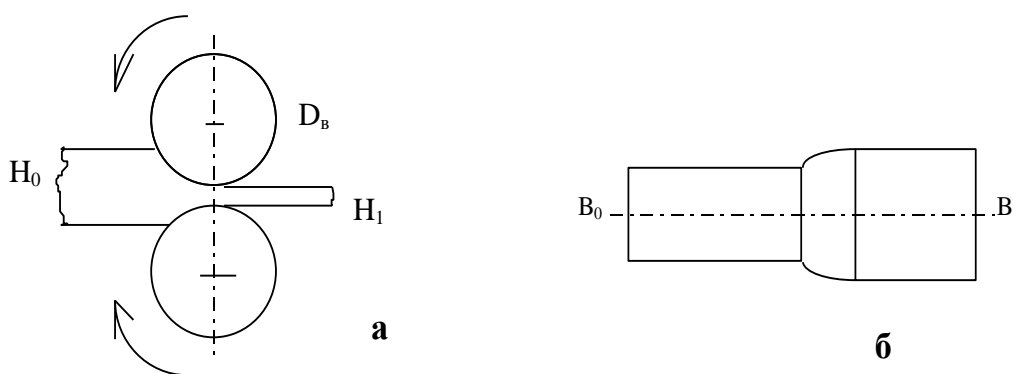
Схема процесса прокатки: а - вид сбоку; б - вид в плане
